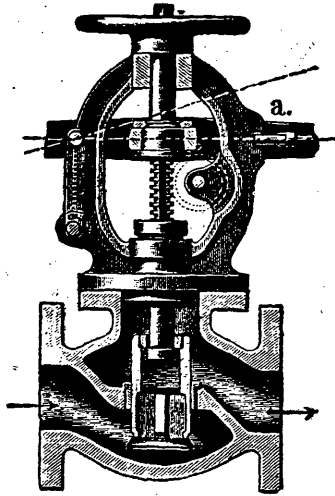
Aparato Dicker y Werneburg para cierre automático de tubos de vapor.
